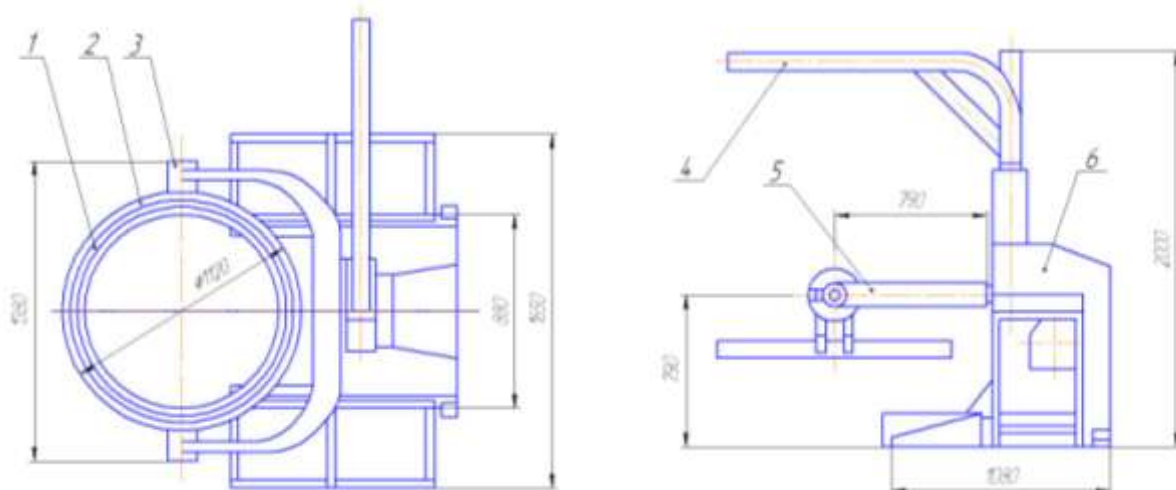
Стенд для разборки и сборки V- образных двигателей (Модель 6501-72)
